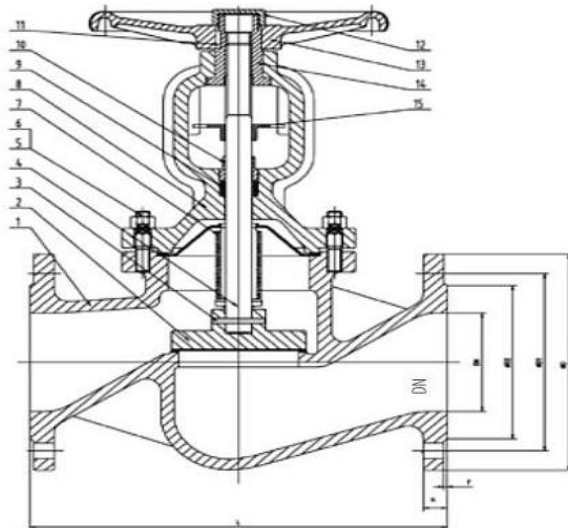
Запорный вентиль 1 – корпус; 2 – золотник; 3 – шплинт; 4 – шток;
